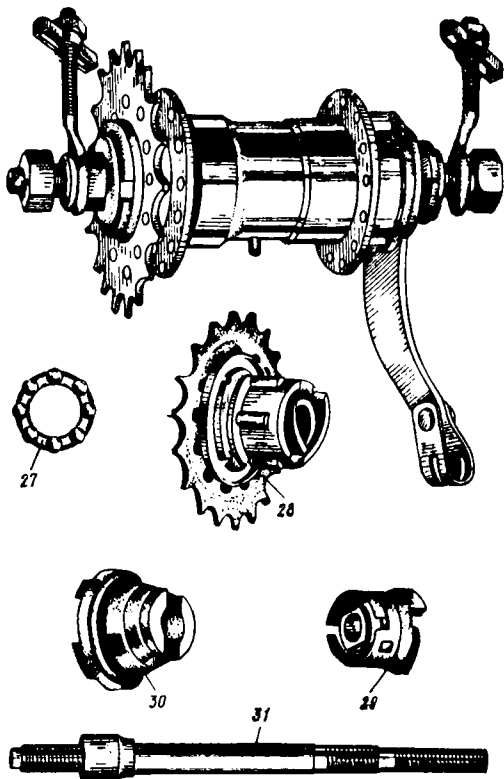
Детали втулки заднего колеса тормозной со свободным ходом:
